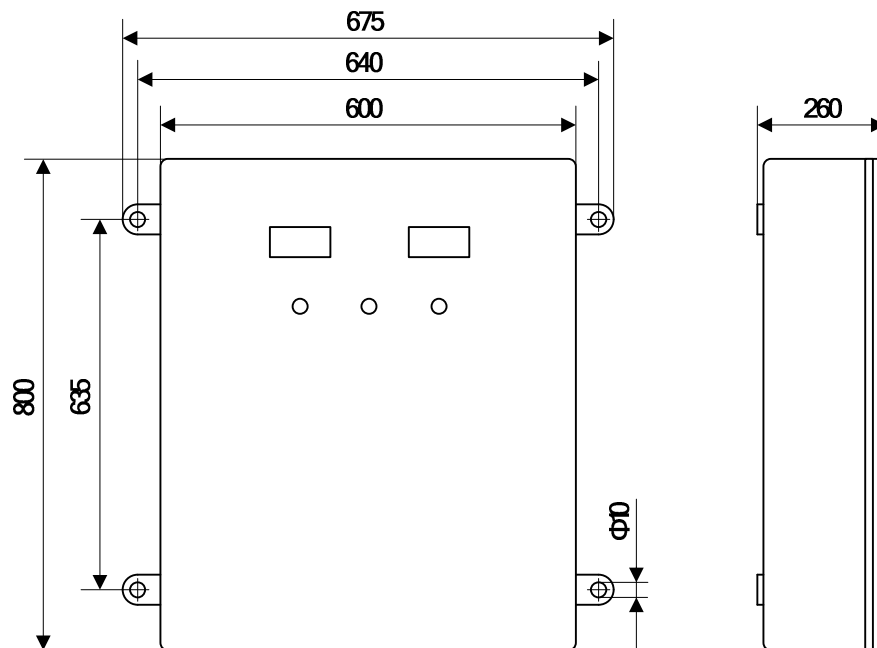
Габаритные и присоединительные размеры БПНС
